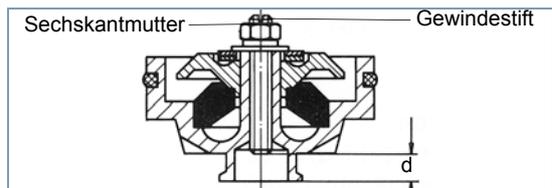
Maß d (Gerät mit einer Gummifeder)
